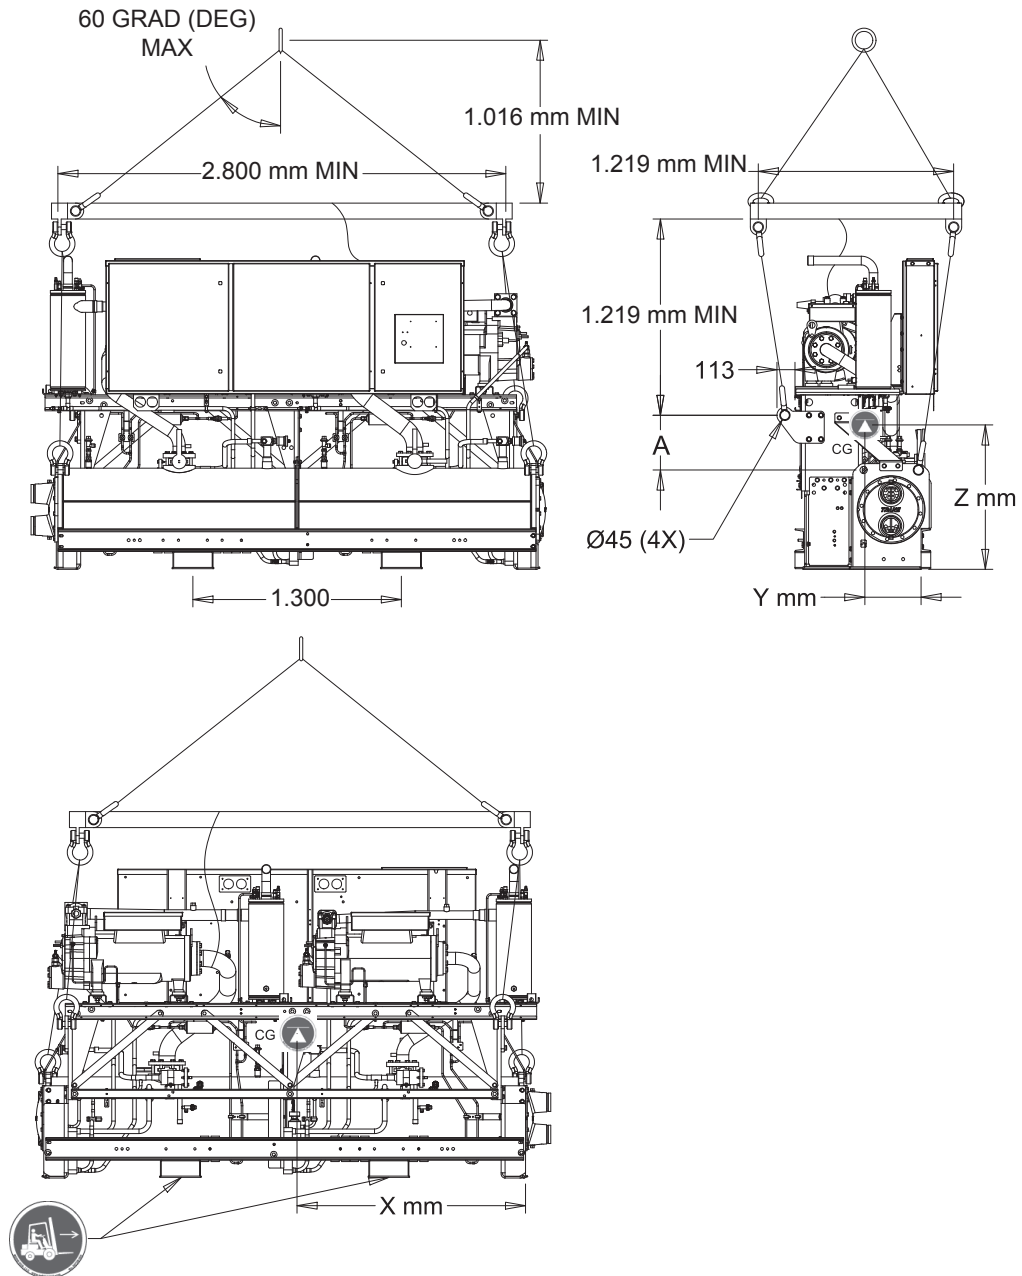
Anschlagen der RTWD-Maschinen (alle Angaben in mm)
